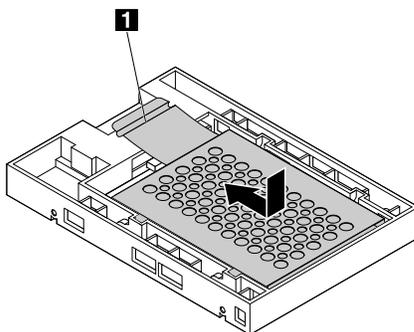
Установка металлической скобы в пластмассовую раму конвертера
